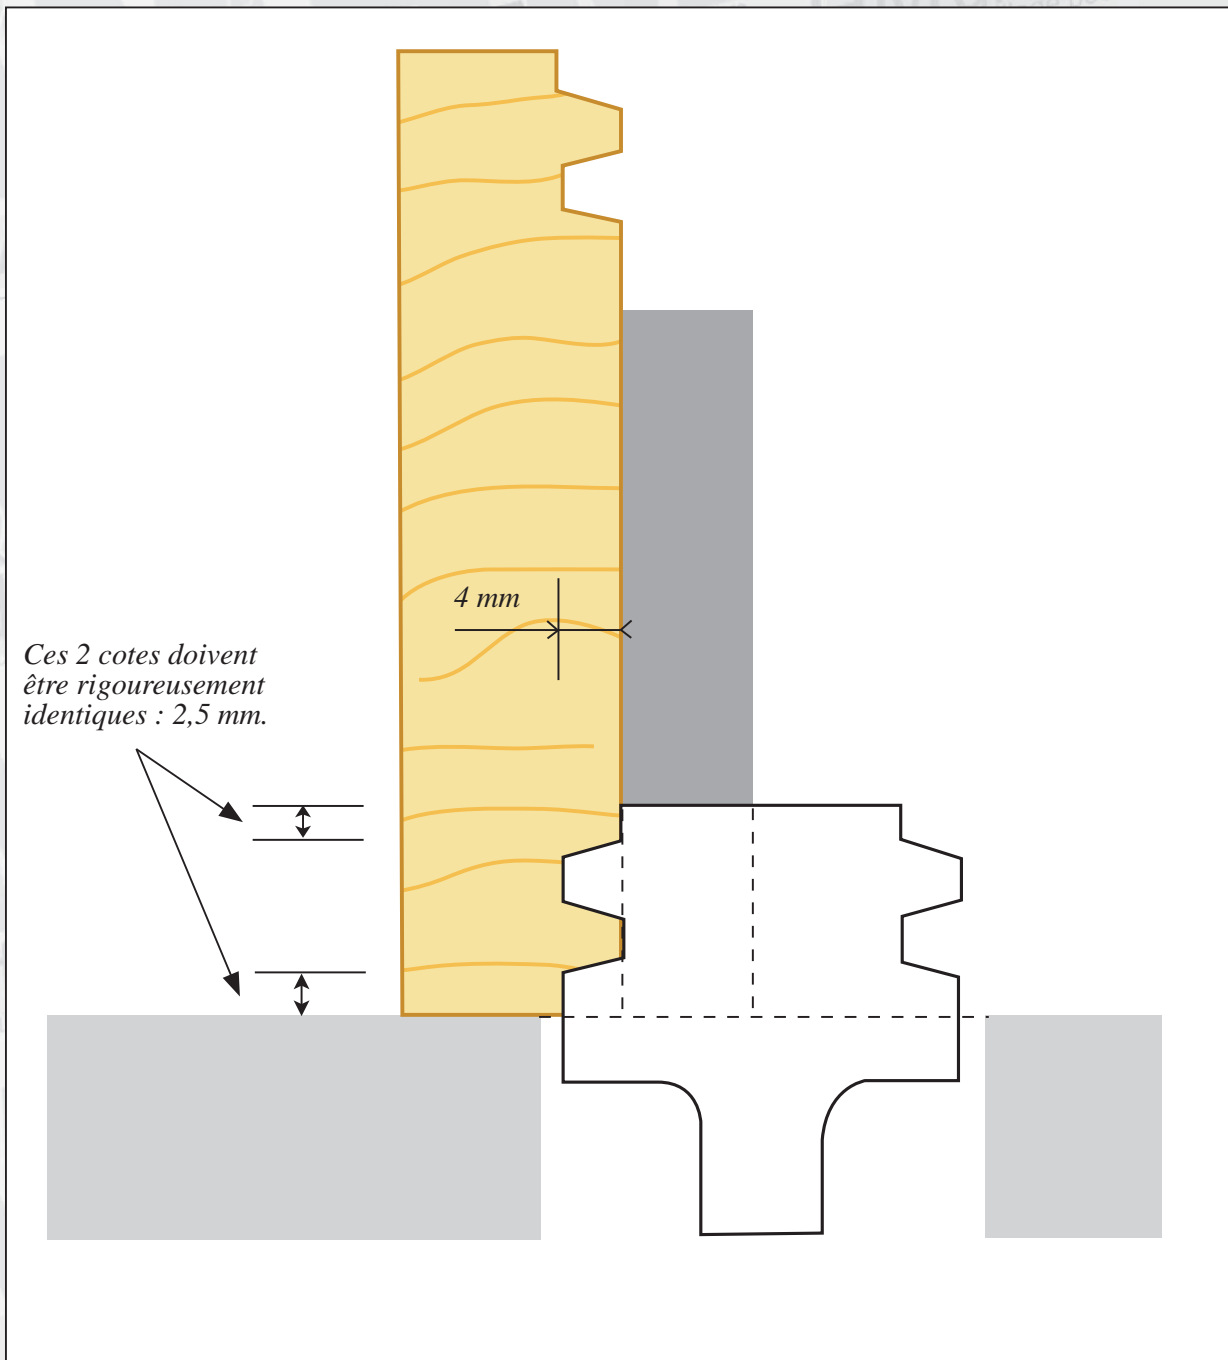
réglage de la fraise pour l'usinage des côtés de tiroir
